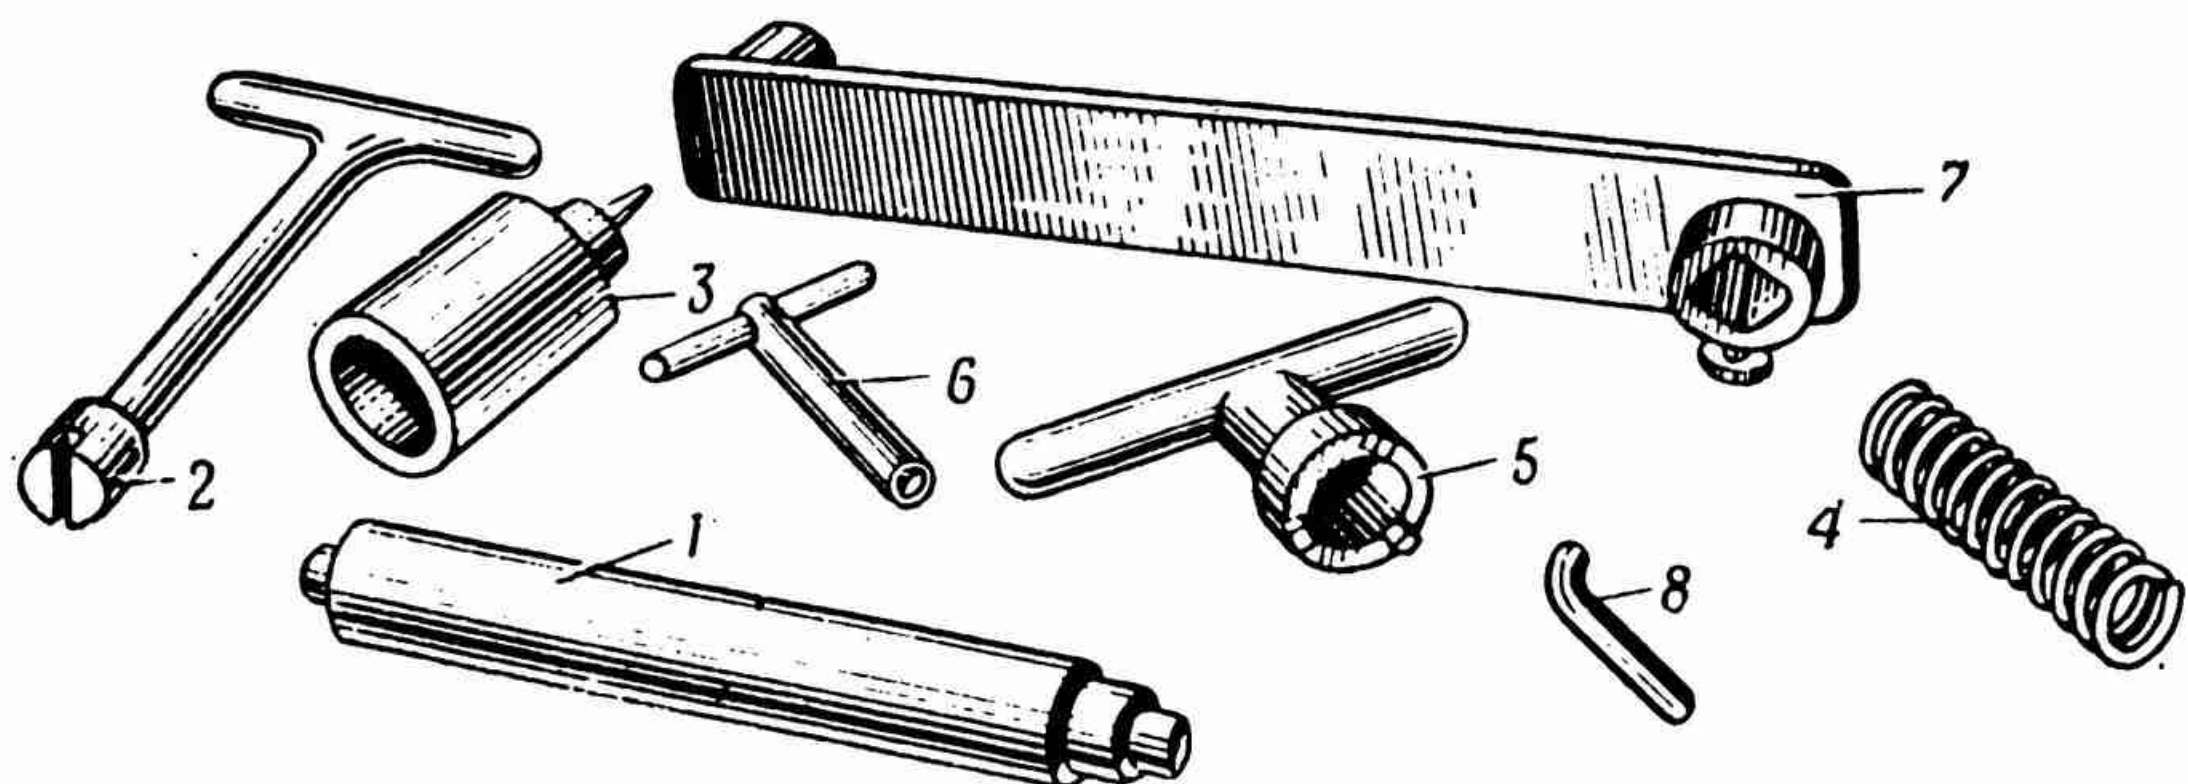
Орудийный комплект ЗИП, укладываемый в сверток для инструмента:
